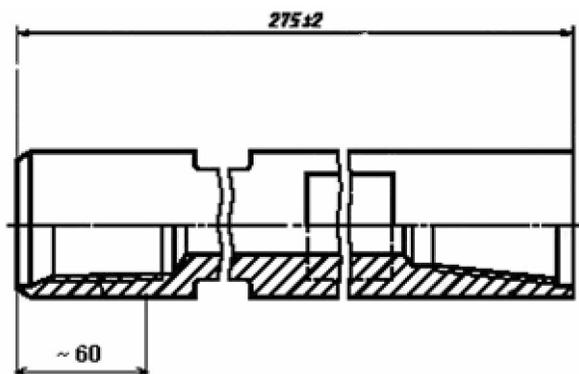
Схема излома муфты со стороны замковой резьбы
